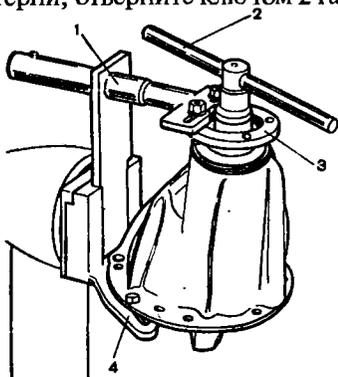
Отвертывание самоконтрящейся гайки ведущей шестерни: 1 - стопор для фиксирования фланца ведущей шестерни; 2 - торцовый ключ; 3 - фланец ведущей шестерни; 4 - кронштейн для крепления редуктора на стенде
